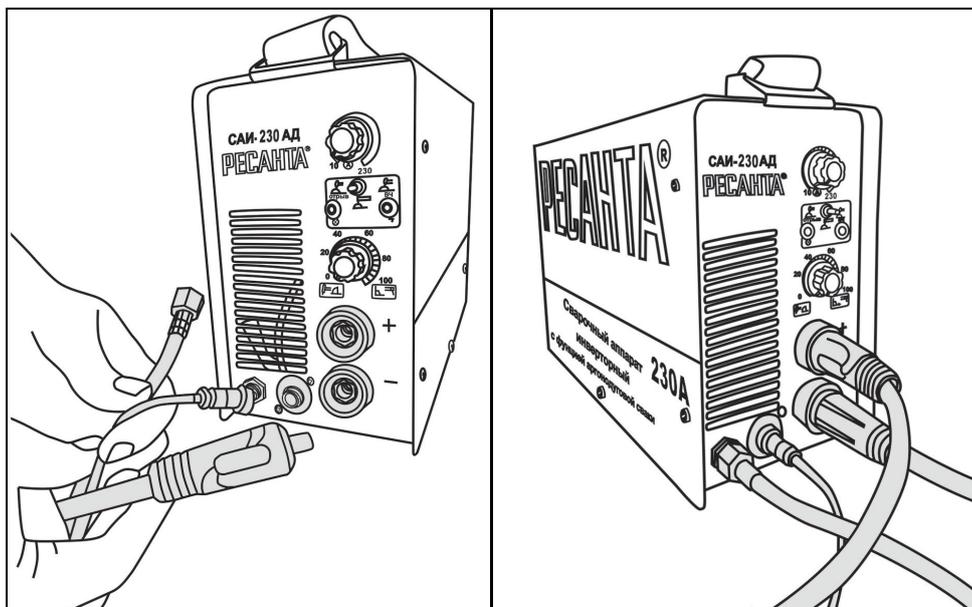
Подключение кабелей в режиме сварки TIG
